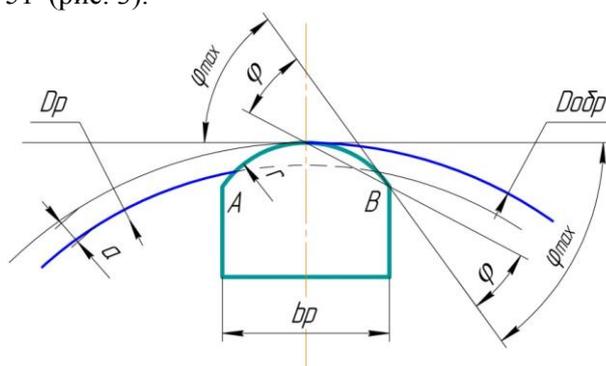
Геометрические параметры зубьев резцовой сборной развёртки
